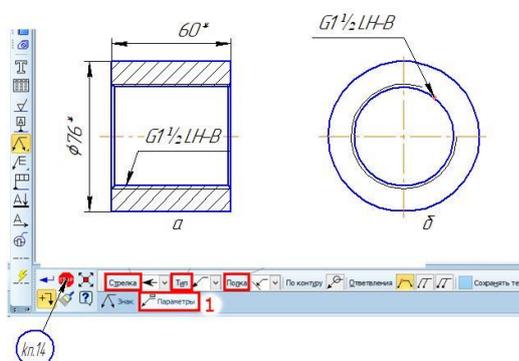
Фрагмент детали с обозначением трубной цилиндрической резьбы
